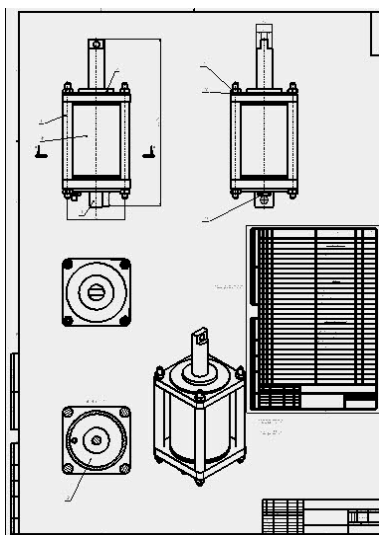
Сборочный чертёж пневмоцилиндра
